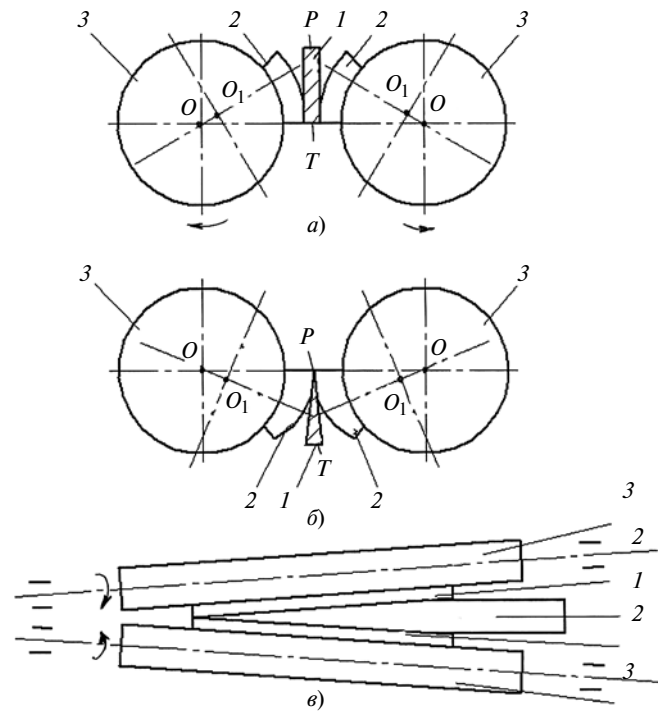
Схема формирования клинка ножа при прокатке в валках со смещенными осями
